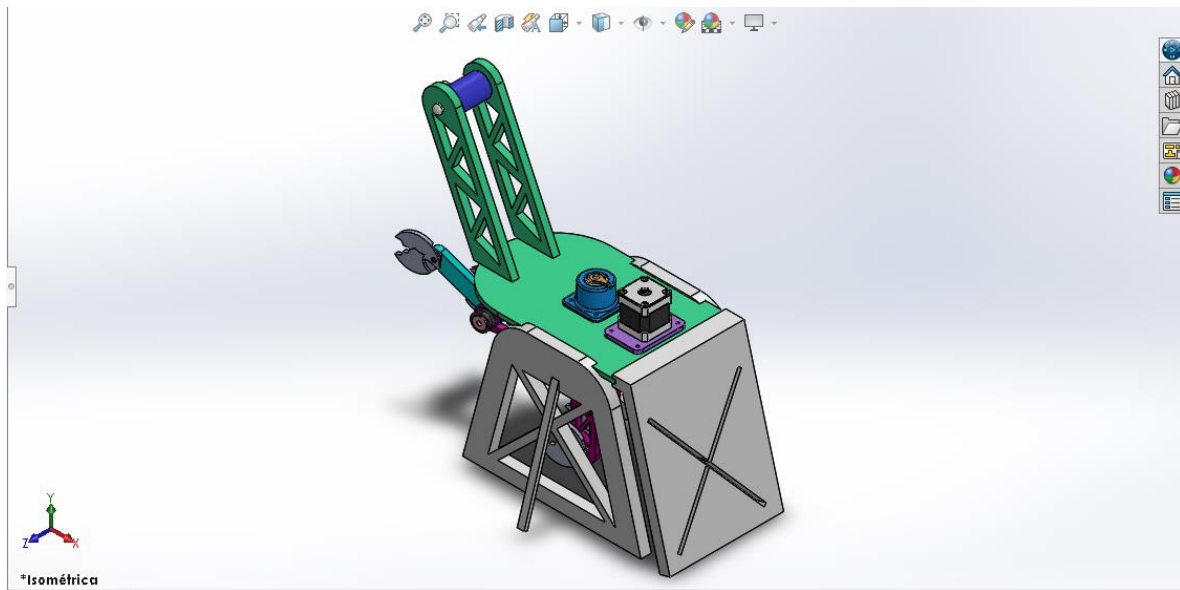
Ensamble de la versión número 1, vista isométrica en SolidWorks. Autor propio.
